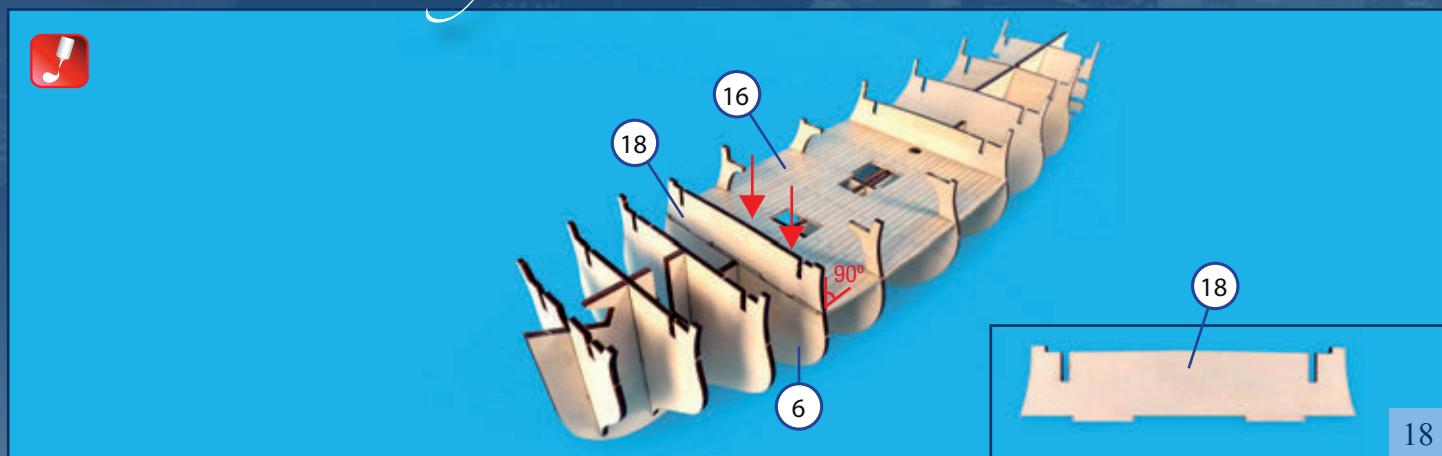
Encaje y pegue la pieza 18 sobre la segunda cubierta 16 y la cuaderna 6. Procure que la pieza 18 guarde un ángulo de 90° respecto a la segunda cubierta.
